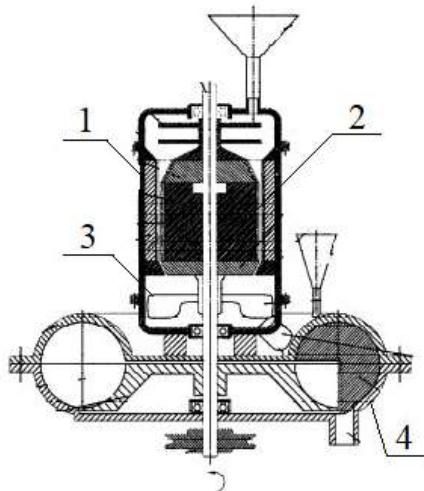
Роторный – центробежный измельчитель: 1- камера измельчения, 2 - ротор, 3 - лопастной питатель, 4 - торообразный смеситель
